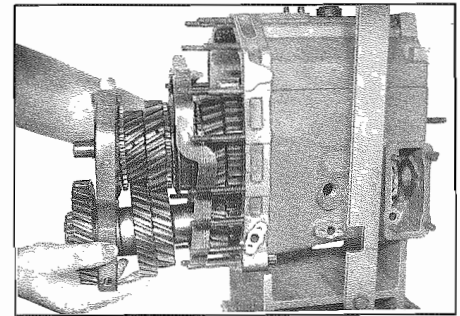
Inserimento dell'albero primario e secondario Inserting the main shaft and countershaft
